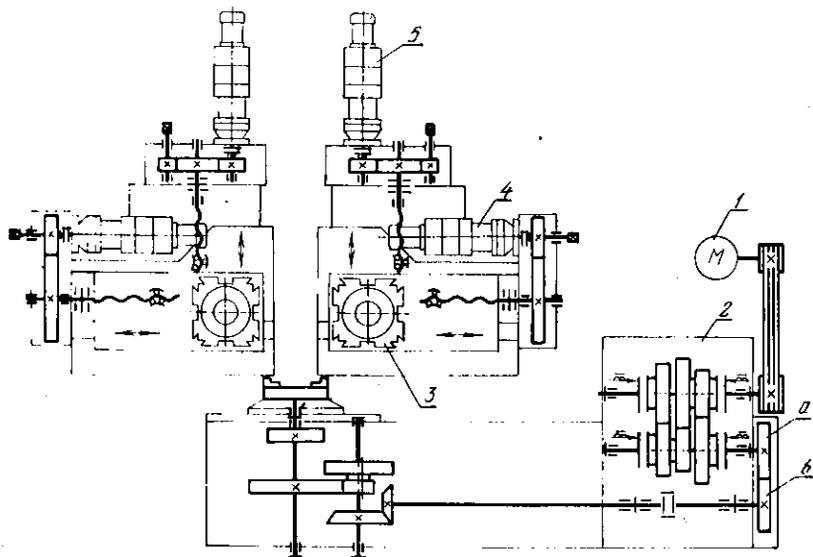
Кинематическая схема токарного полуавтомата с ЧПУ модели 1734Ф3
